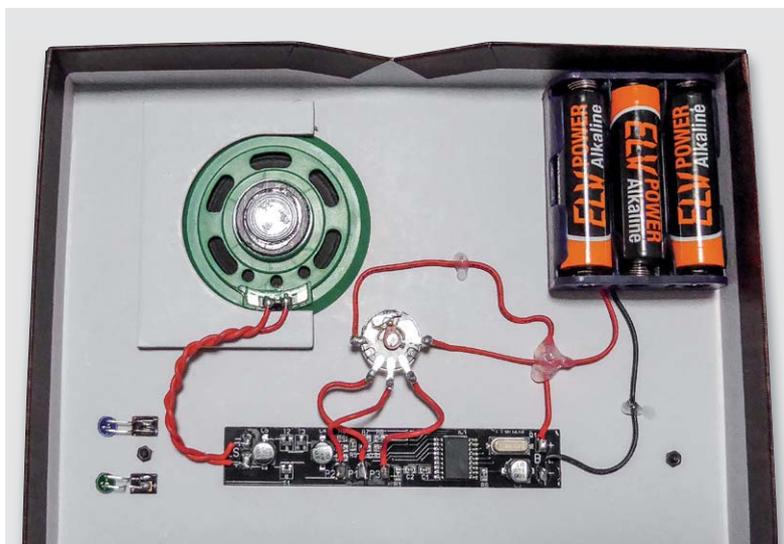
Die Lage und die Verdrahtung aller Bauteile im Gehäuse
